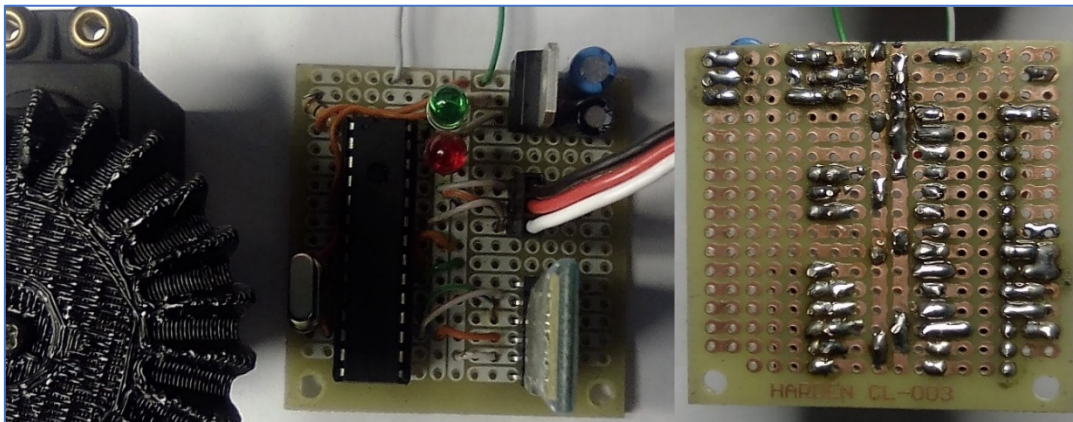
Circuito montado y soldado en placa fenólica perforada
